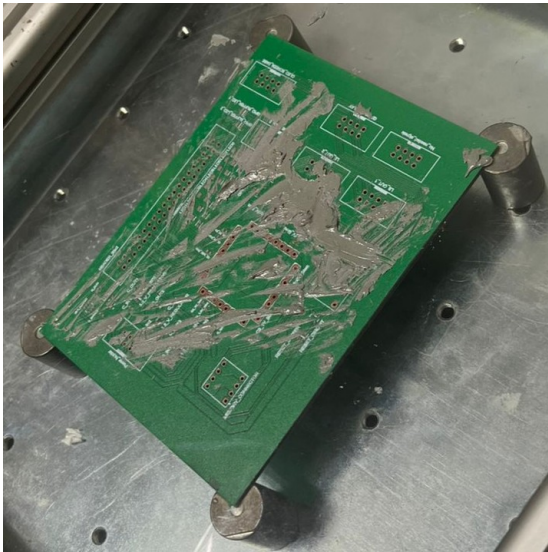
Aplicación de la pasta de soldadura usando un *stencil*.
